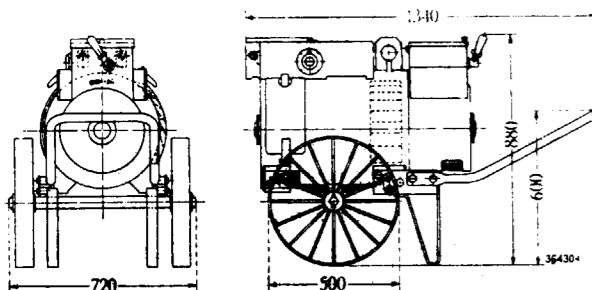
Croquis acotado de un grupo de soldadura.
